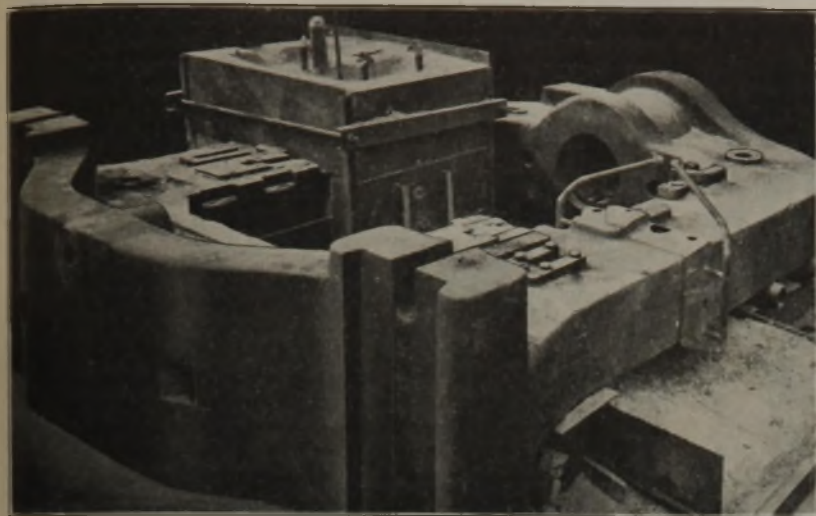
Umkleidung des Bruches mit einer Blechlasche (rechts); links die fertige Form.
